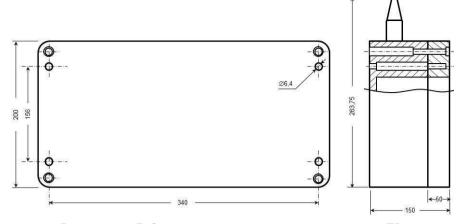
Габаритные и присоединительные размеры ПВ
